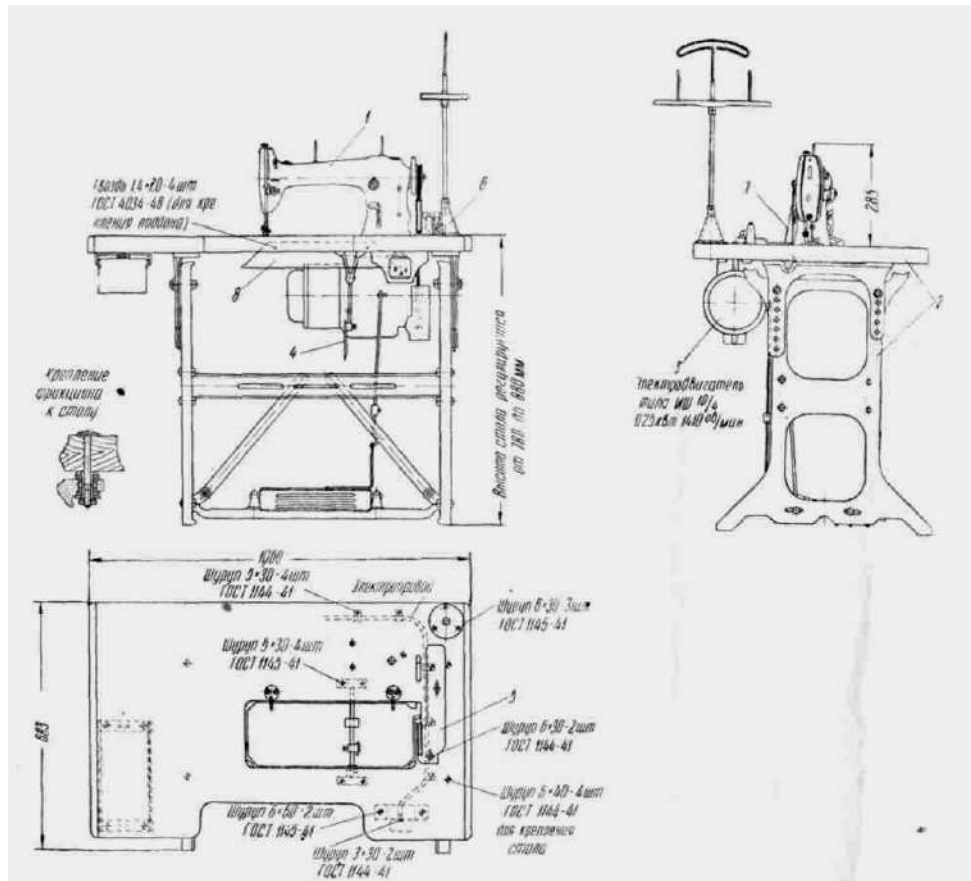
Монтажный чертеж швейной машины класса 1022-М: 1— головка машины; 2 — стол промышленный; 3— фрикцион с электродвигателем; 4 — коленный рычаг; 5 — автоматическая моталка; 6 — стойка для катушек; 7 — ограждение ремня; 8 — поддонник
